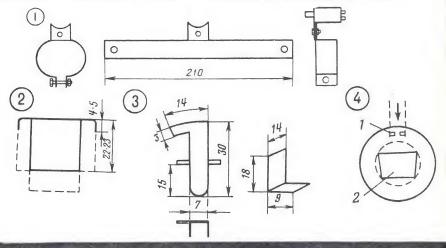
Держатель. Рис. 2. Так обрезается пробка для ротора распределителя. Рис. 3. Две детали из жести: слева— бегунок; справа— вкладыш. Рис. 4. Самодельный ротор готов: 1— загнутые «усики» бегунка; 2
